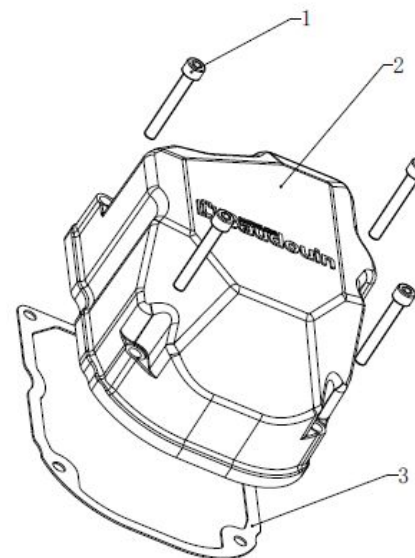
Сборочный чертеж крышки головки блока цилиндров 16М33
